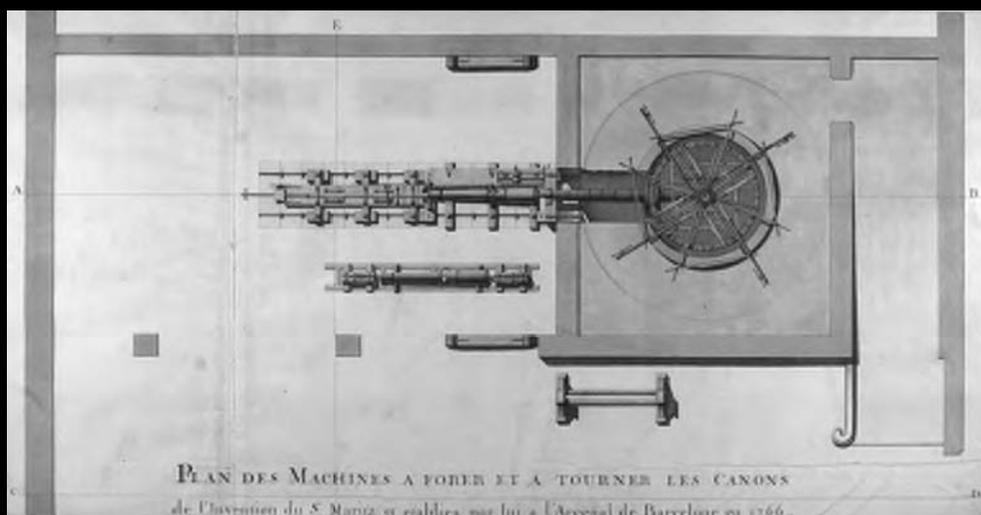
Planta de la máquina para barrenar y tornear cañones.
